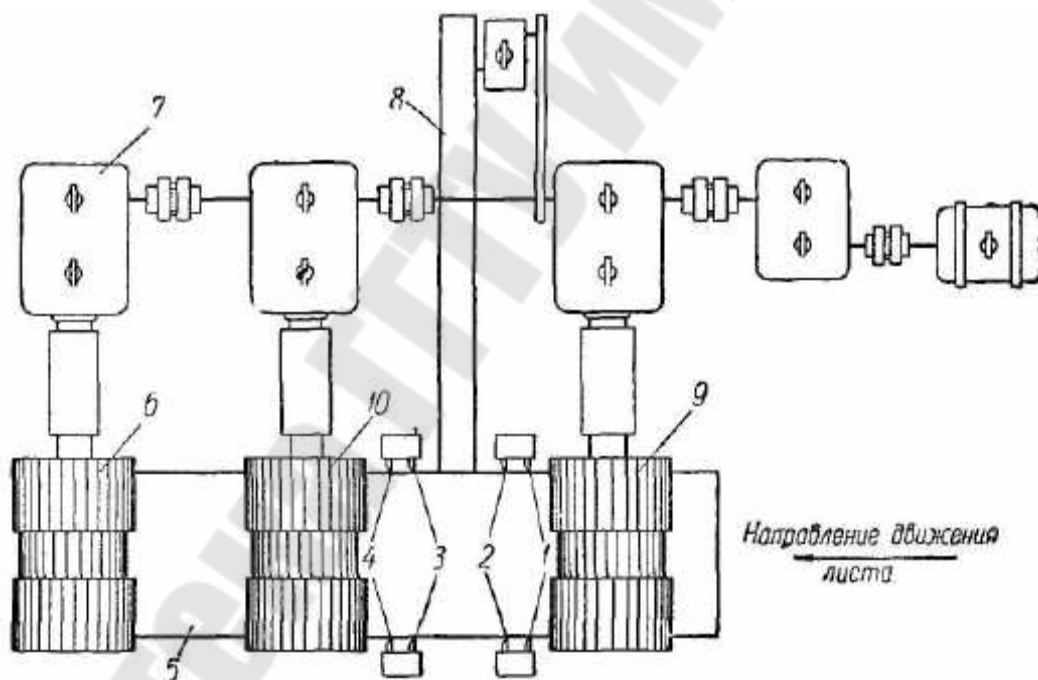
Схематическое изображение кромкострогального станка: 1, 2, 3, 4 – резцы; 5 – лист; 6, 9, 10 – ведущие валки; 7 – редуктор; 8 – транспортер
